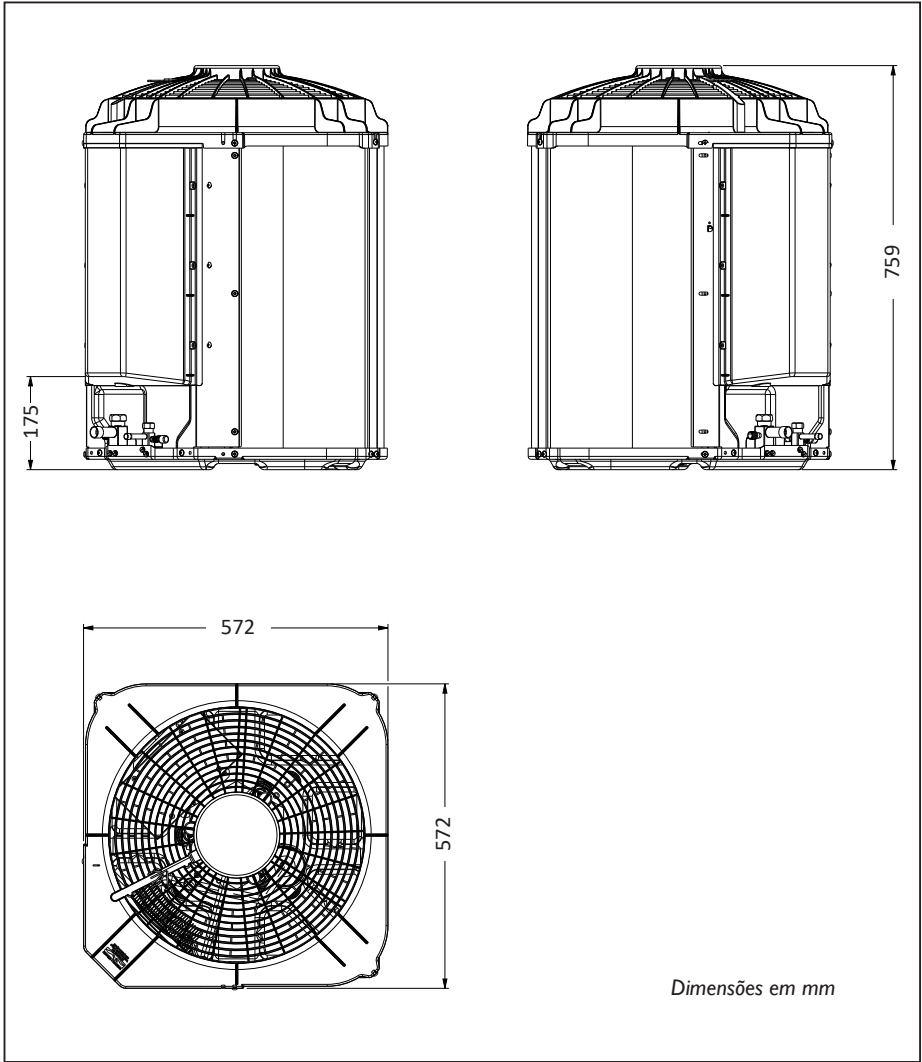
DIMENSIONAL UNIDADES CONDENSADORAS 38C_VB30 / 38C_VB36
